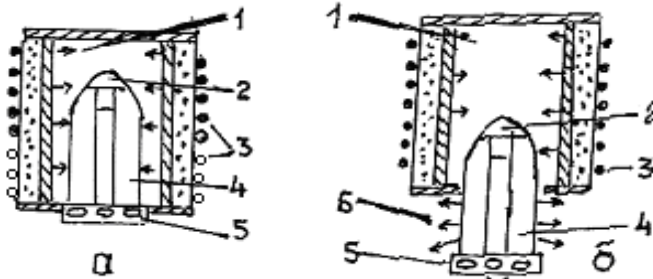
Схемы процессов направленной кристаллизации: а - статичное положение отливки; б - вытягивание отливки из зоны нагрева. 1 – направление теплоизлучения со стороны нагревателей; 2 – прибыль; 3 – витки индуктора (зачерненные- под током, светлые – обесточенные); 4 – керамическая оболочка с отливкой; 5 – водоохлаждаемый холодильник; 6 – направление теплоотвода от формы
